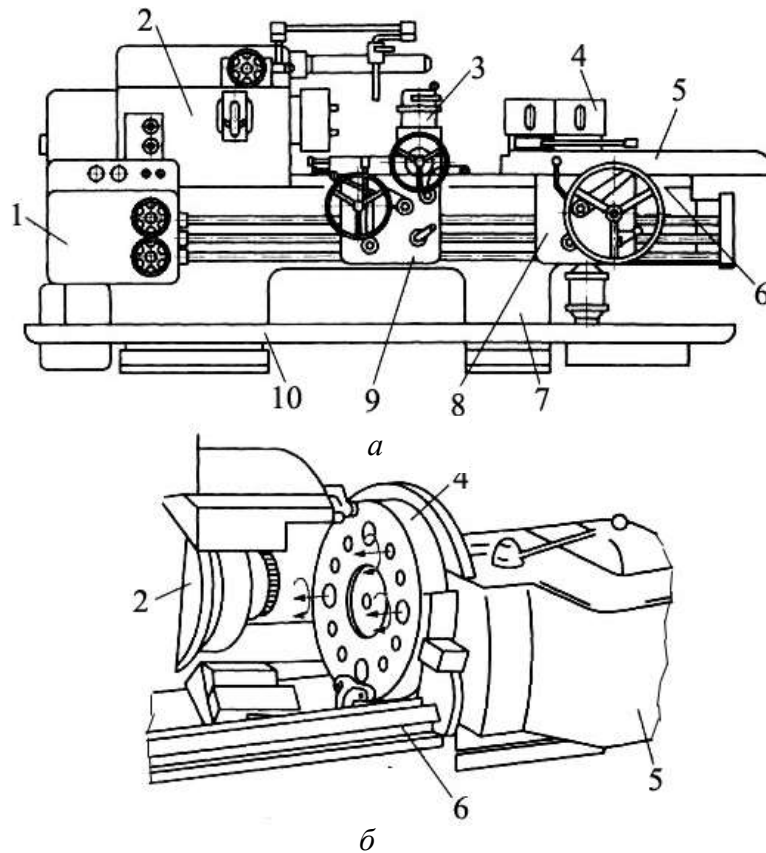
Токарно-револьверний верстат з вертикальною (а) і горизонтальною (б) віссю обертання револьверної головки:
